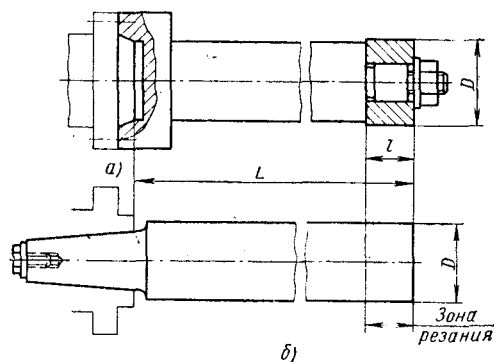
Эскизы образцов для испытания на виброустойчивость:
